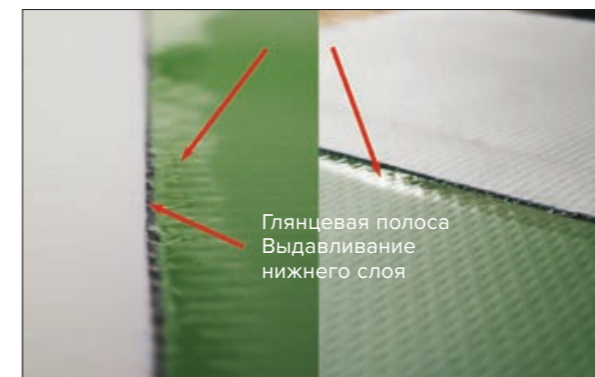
Визуальная проверка качества сварного шва
